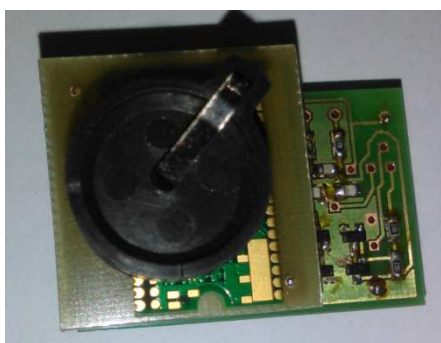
Vyhotovená DPS Main a Channel, přední strana
